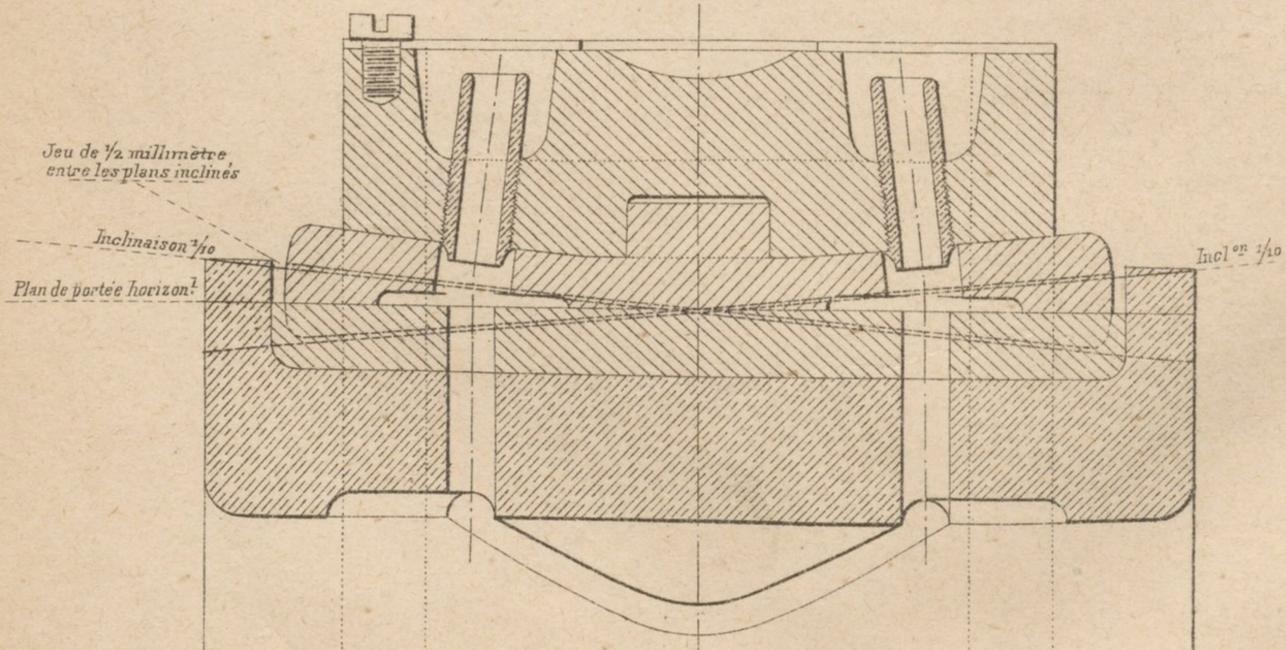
Boîte de graissage d'avant à plans inclinés.
